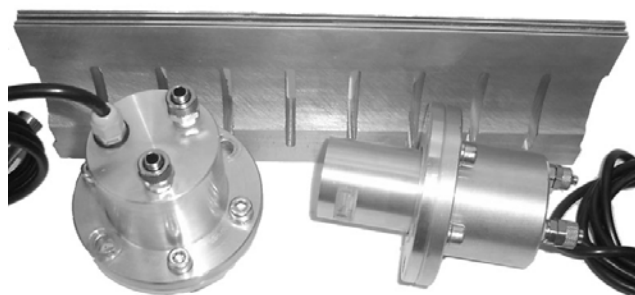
Рабочий сварочный инструмент ультразвуковой колебательной системы.
